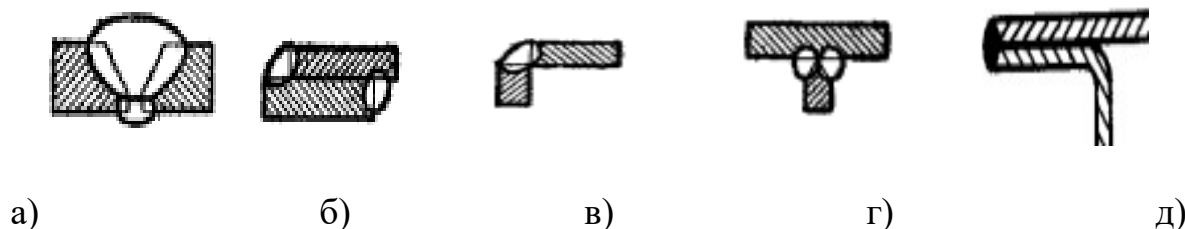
Типы сварных соединений: а) –стыковое; б) – нахлесточное; в) – угловое; г) – тавровое; д) – торцовое
